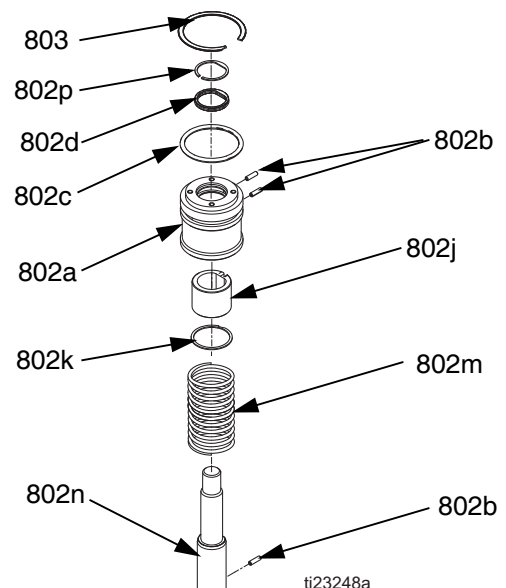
Joint de tige de piston 76,2 mm (3 po.)
